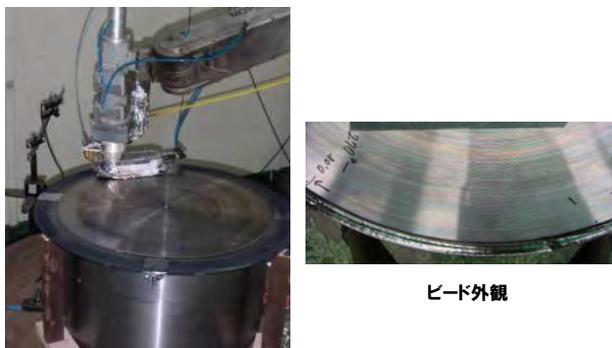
レーザビーム溶接 蓋溶接施工試験実施状況
